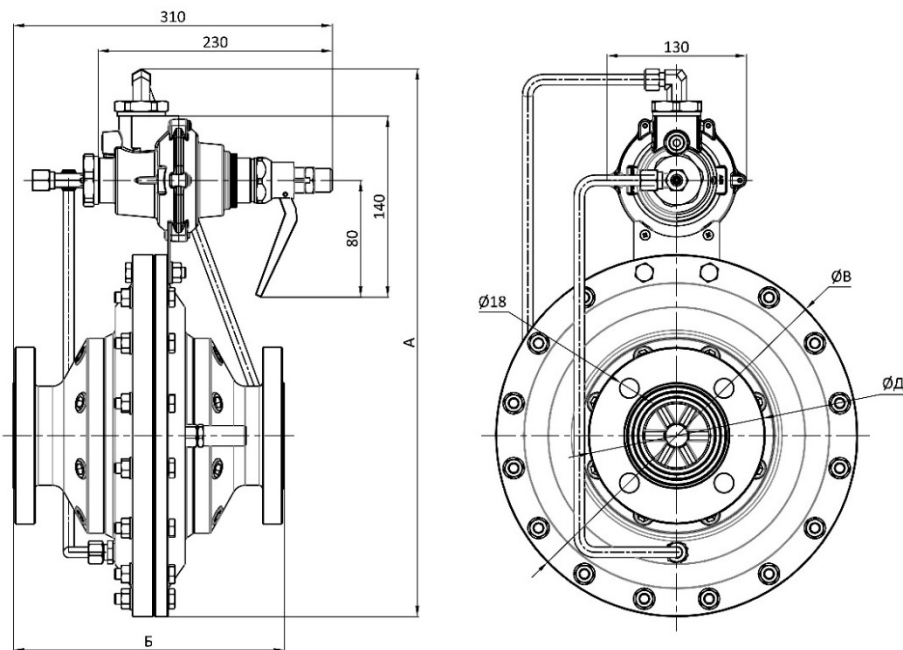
Габаритные размеры ПСК «РЕД-П»
